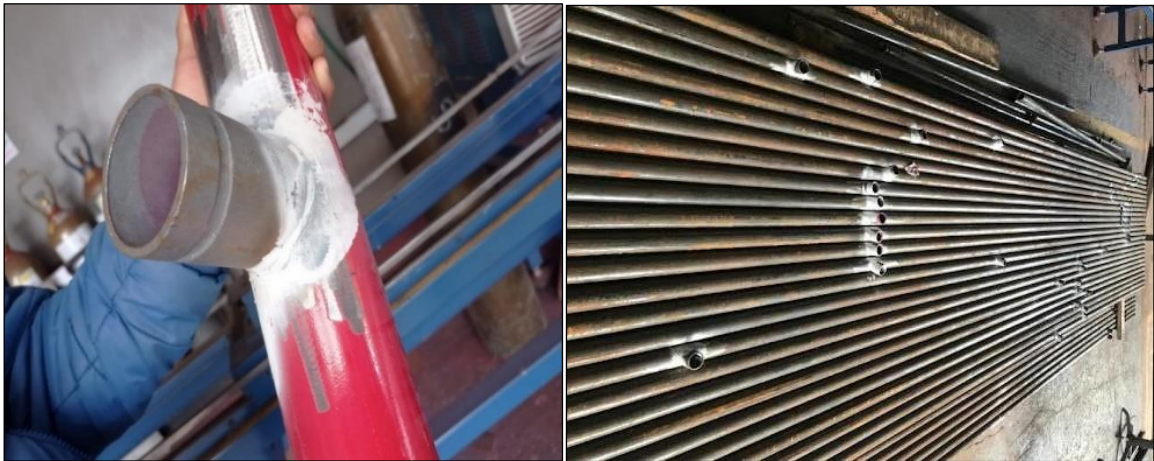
Accesorio tipo outlet unido a tubería por medio de soldadura MIG
